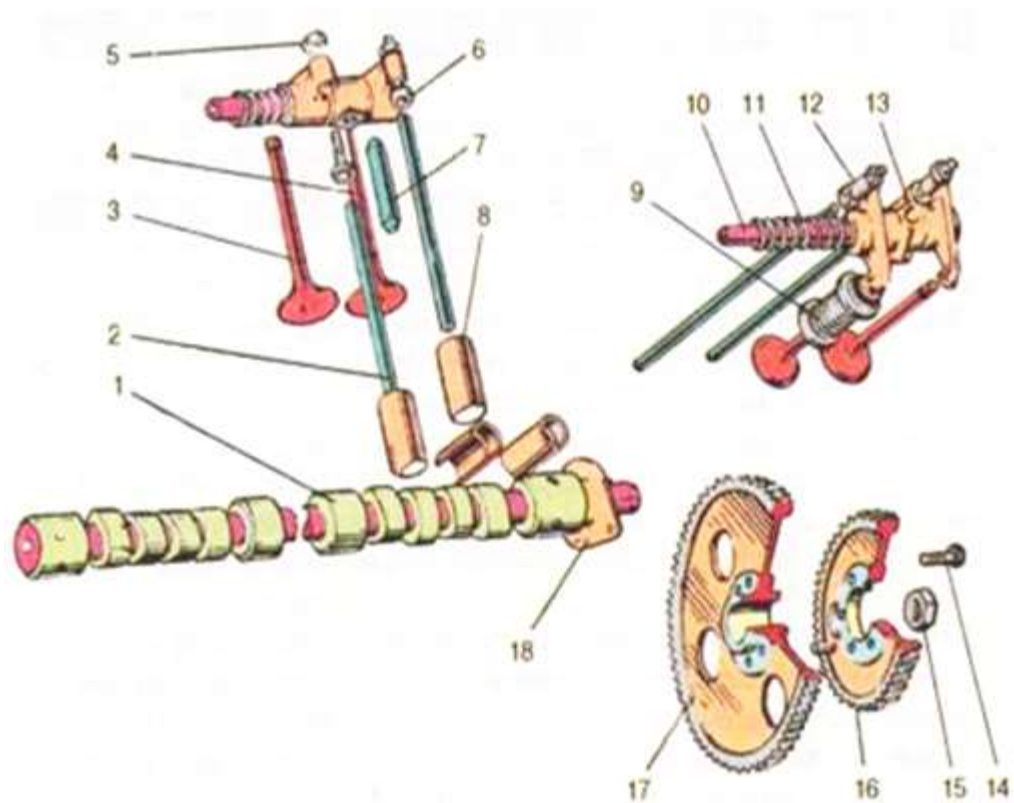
Газорозподільний механізм дизеля СМД-60:
